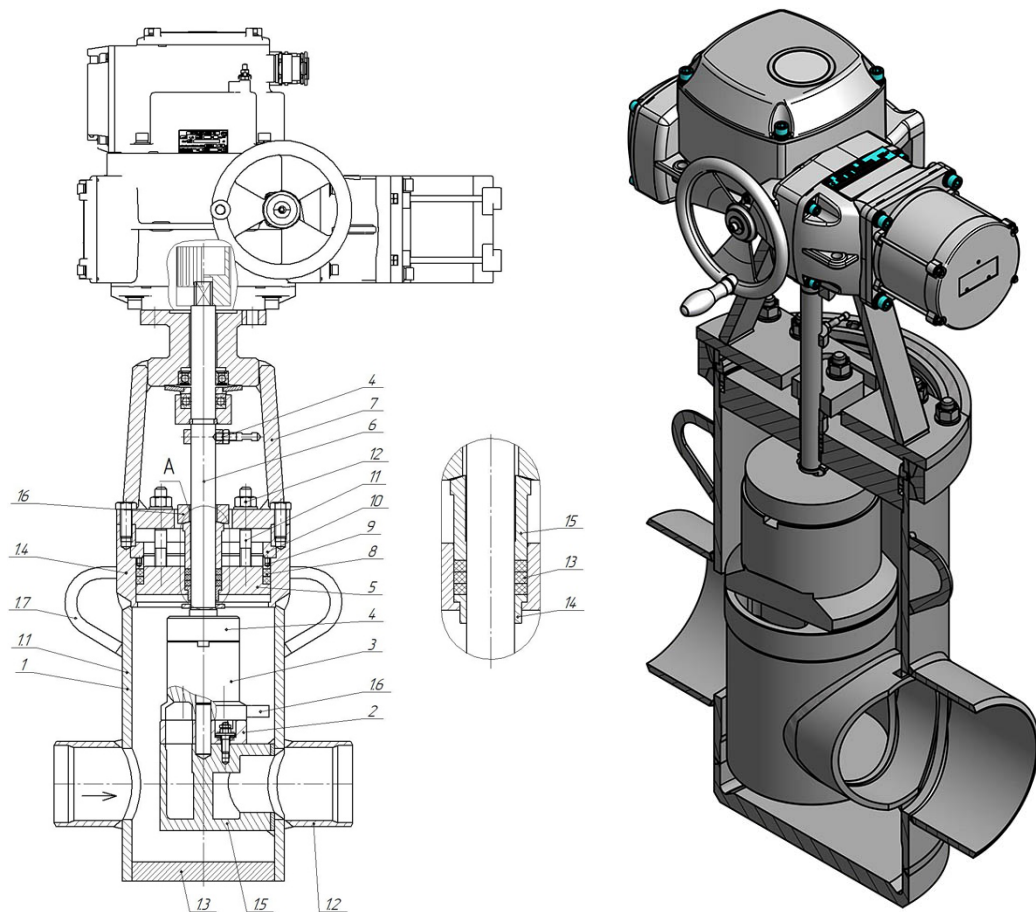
Клапан запорно-регулирующий дисковый КРЗд
